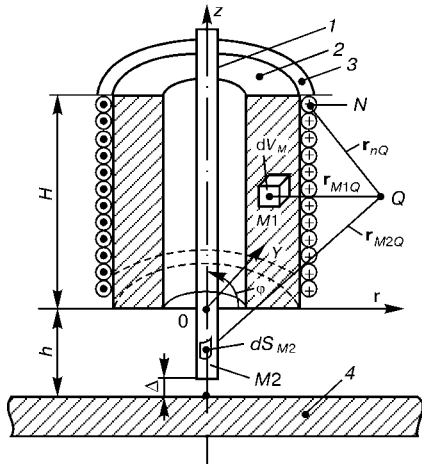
Схема соленоида, генерирующего ПРМП: 1 — сварочная проволока; 2 — сердечник; 3 — витки катушки (медь); 4 — изделие
